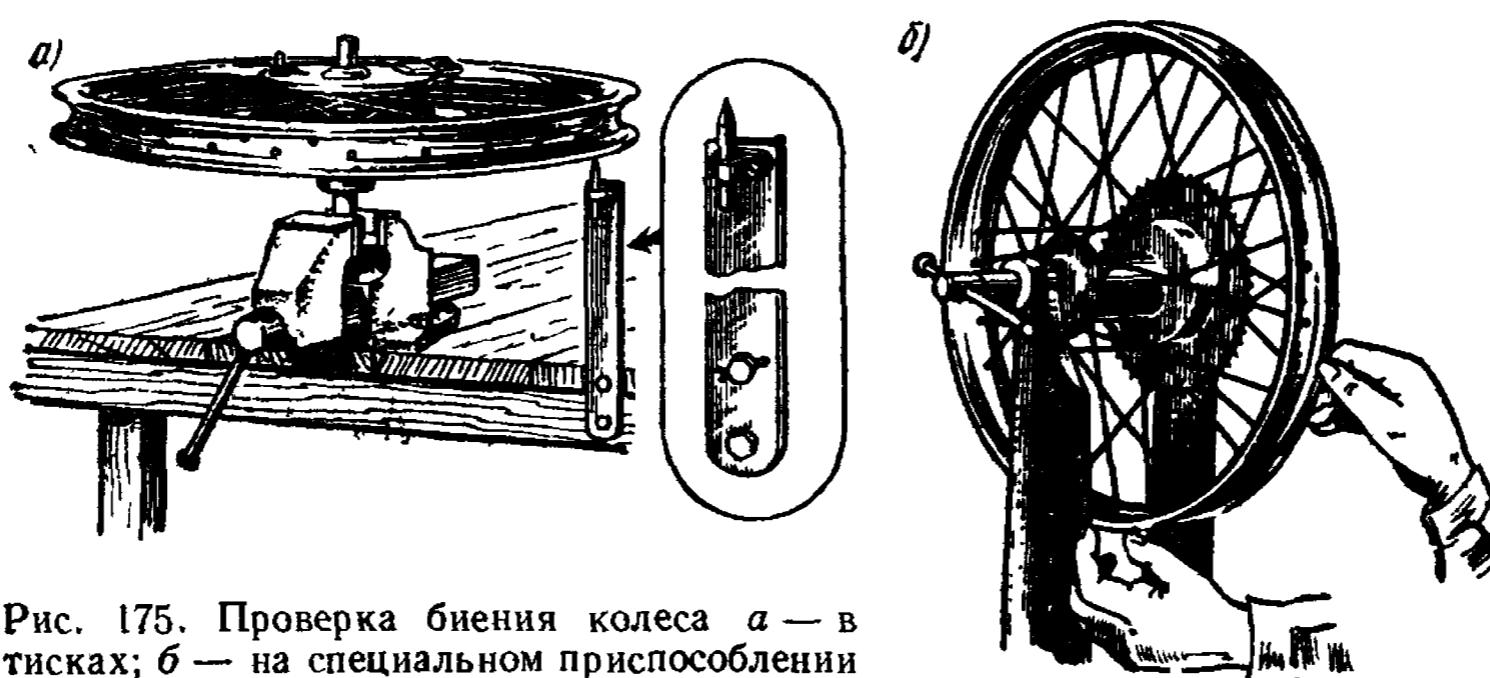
Проверка биения колеса *а* — в тисках; *б* — на специальном приспособлении
